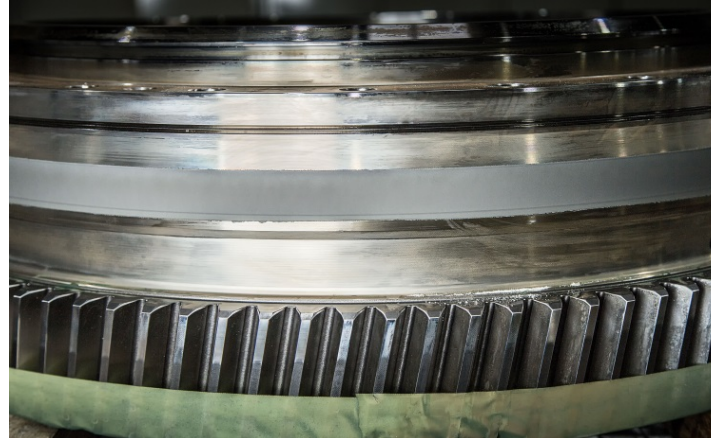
Neben der Größe des Bauteils spricht die lokal eng begrenzte Bearbeitung für die Beschichtung der stark beanspruchten Dichtsitze durch Plasmaspritzen.
